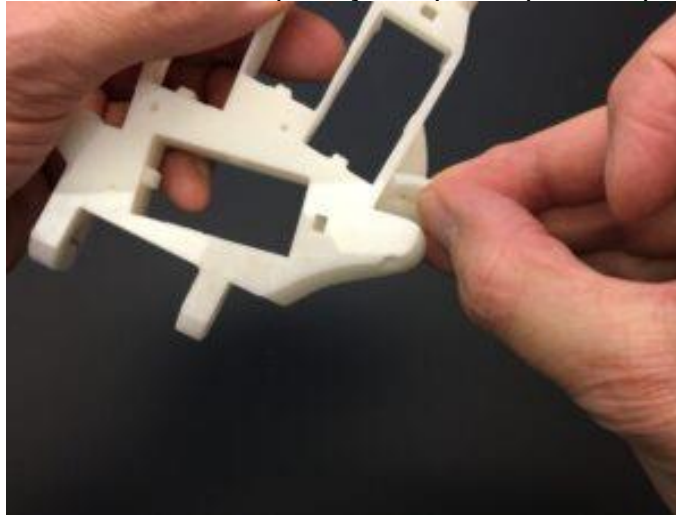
Alinhe a engrenagem principal e o RotaWrist3.
